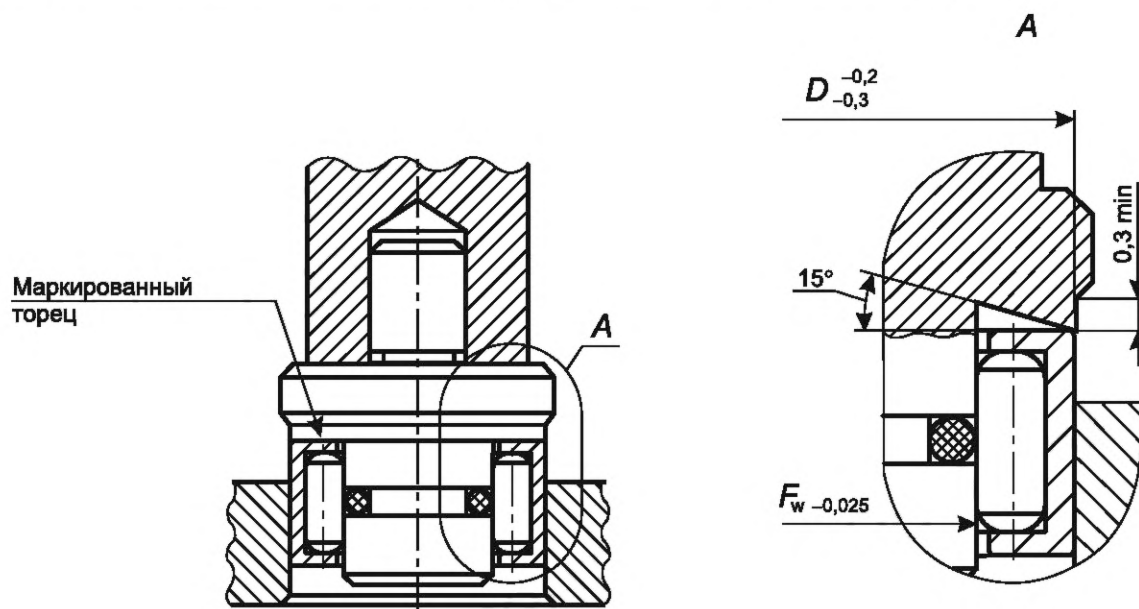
Оправка для монтажа подшипников в корпусе
